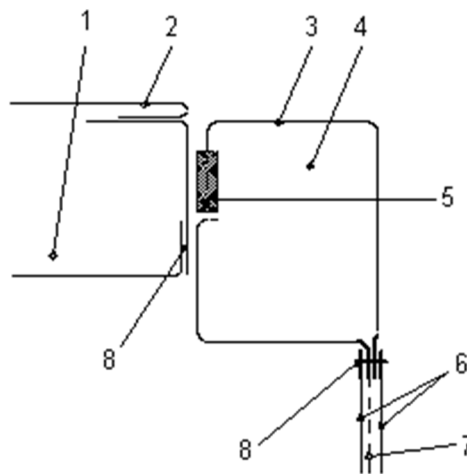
4. Фрагмент двері робочої камери: 1 - стінка робочої камери; 2 - кожух; 3 - металевий корпус двері; 4 - дросельна порожнину; 5 - додатковий поглинач енергії СВЧ; 6 - полімерна плівка; 7 - перфорація; 8 - зварювання.
